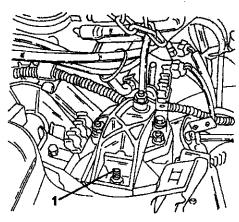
Вид подвески со стороны привода газораспределительного механизма на двигателе типа XU. Гайка (1) затягивается моментом 45 нм.
